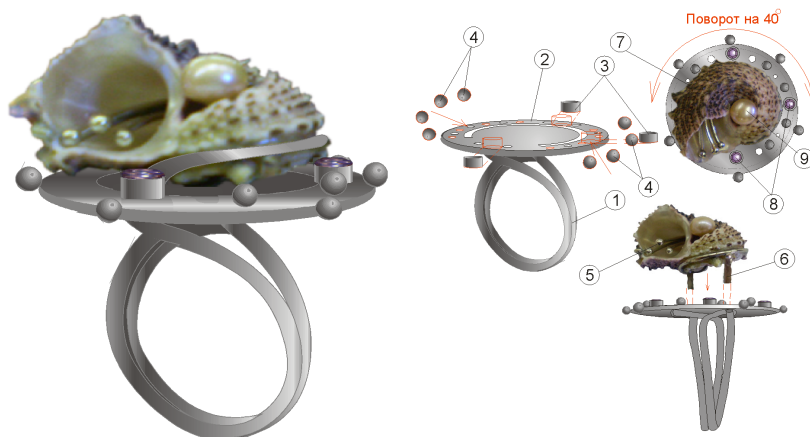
Конструкция кольца "Ракушка": 1 – шинка кольца; 2 – полусферическая заготовка, круглой формы; 3 – заготовка круглой формы Ш4; 4 – заготовка круглой формы Ш1,5; 5 – каст для камня Ш3мм; 6 – каст для декоративной вставки; 7 – штифт; 8 – камень Ш3,0 мм; 9 – камень Ш5,0 мм; 10 – декоративный элемент
